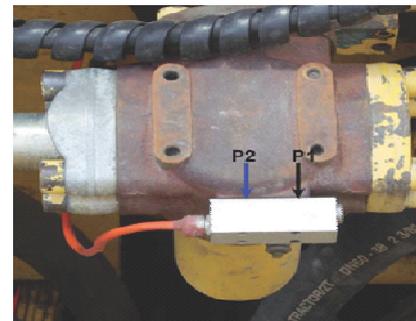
Housing, Magnet Piston dan Spring Piston.
